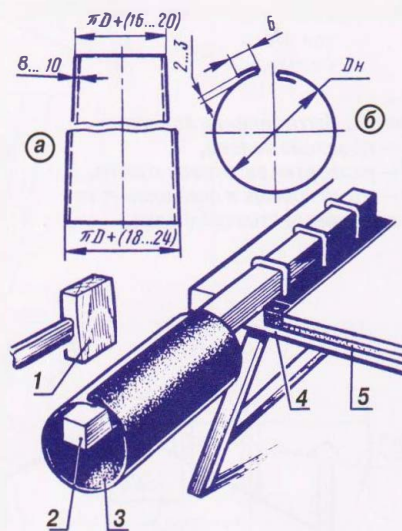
Изготовление патрубка дымохода: а — заготовка, б — свёртывание цилиндра, соединение кромок в одинарный лежащий фальц; 1 — киянка, 2 — брус-оправка, 3 — патрубок, 4 — верстак, 5 — уголок.
